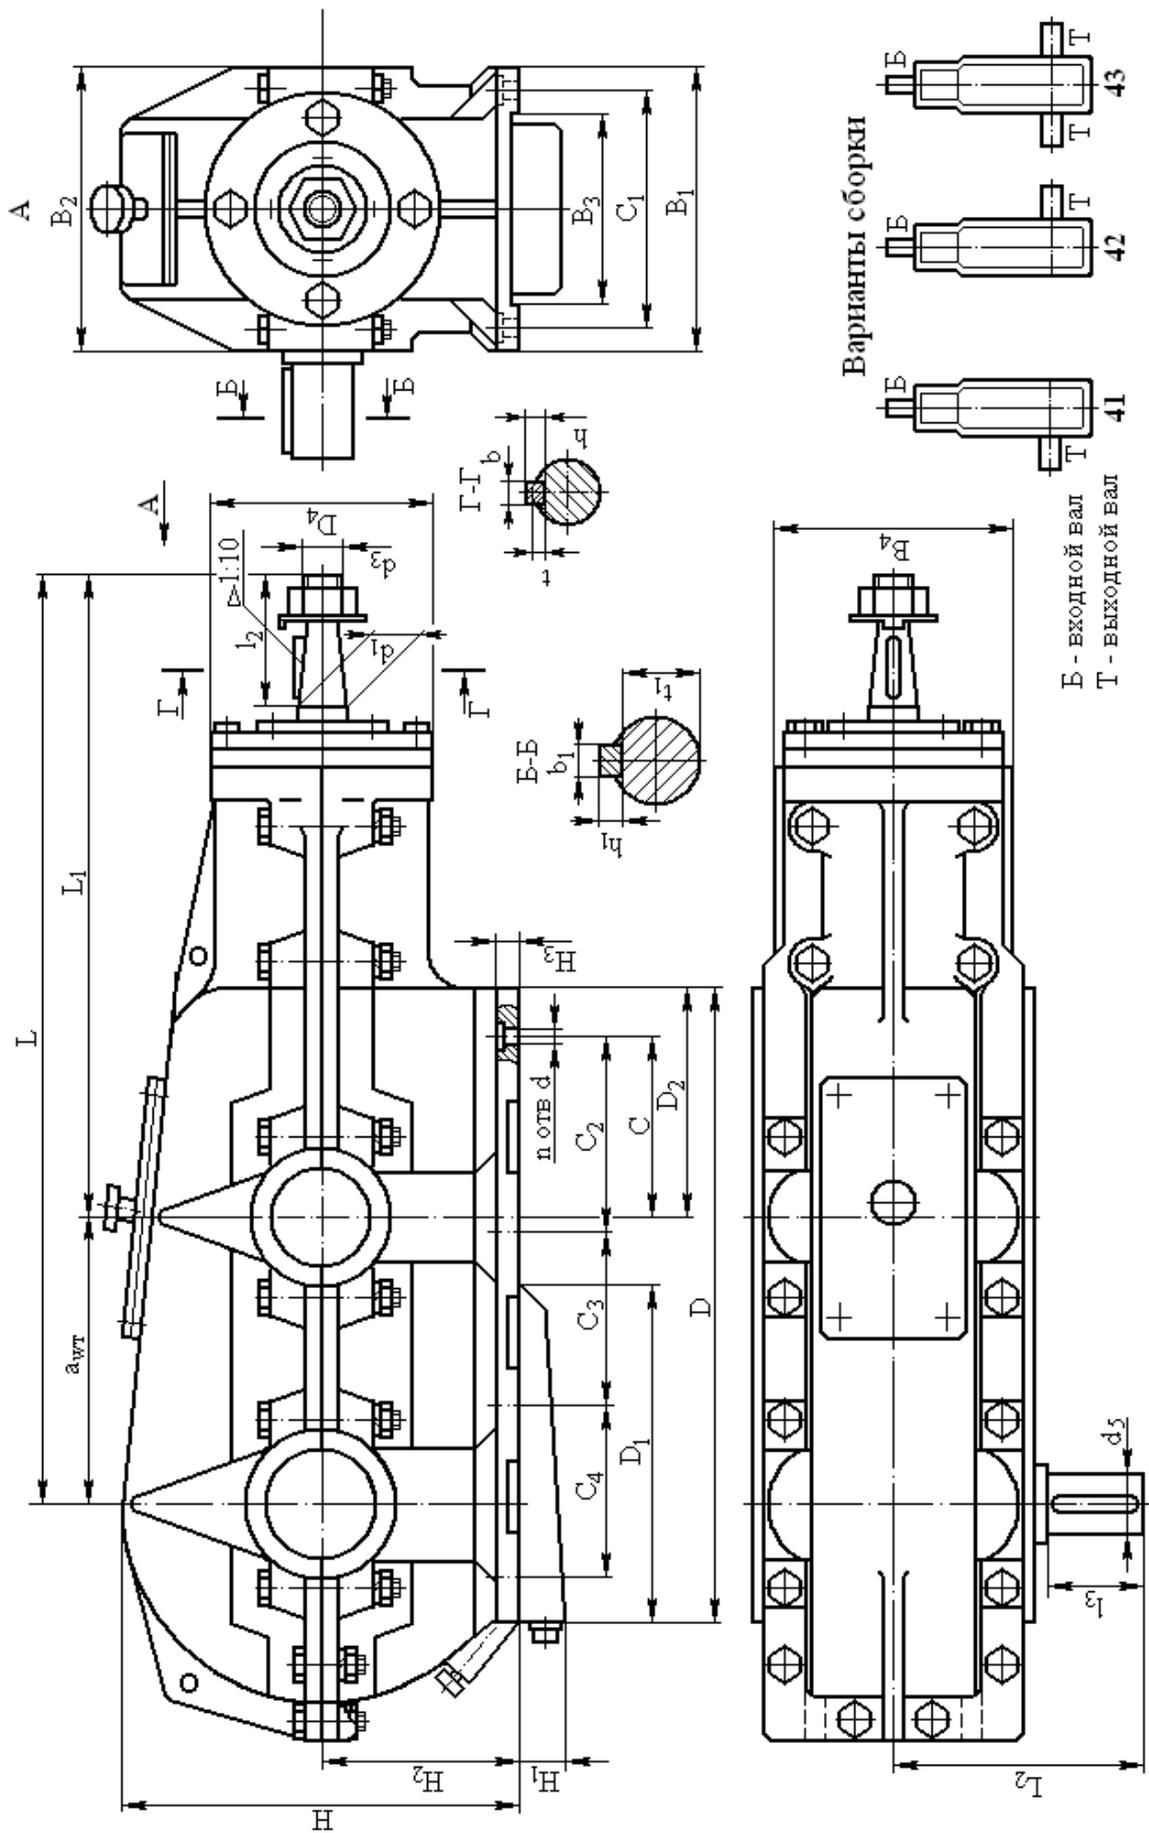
Коническо-цилиндрический двухступенчатый редуктор типа КЦ1
